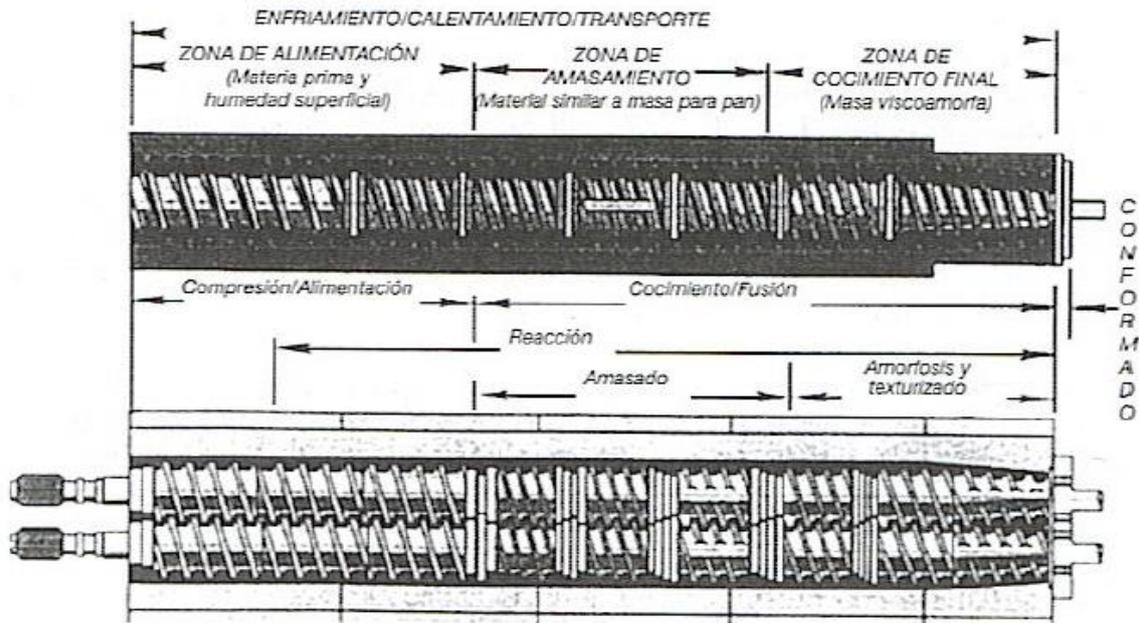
Cortes de un extrusor de un solo tornillo y uno de tornillos gemelos.
